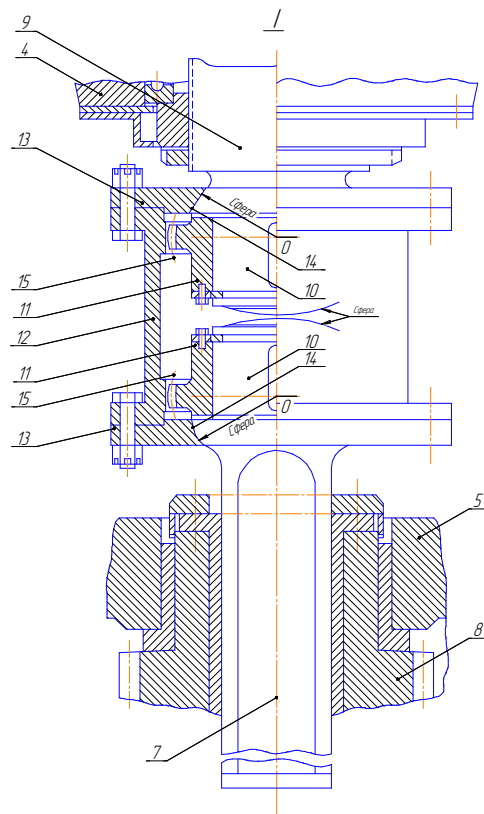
Вид I пристрій для виштовхування злитка з виливниці
